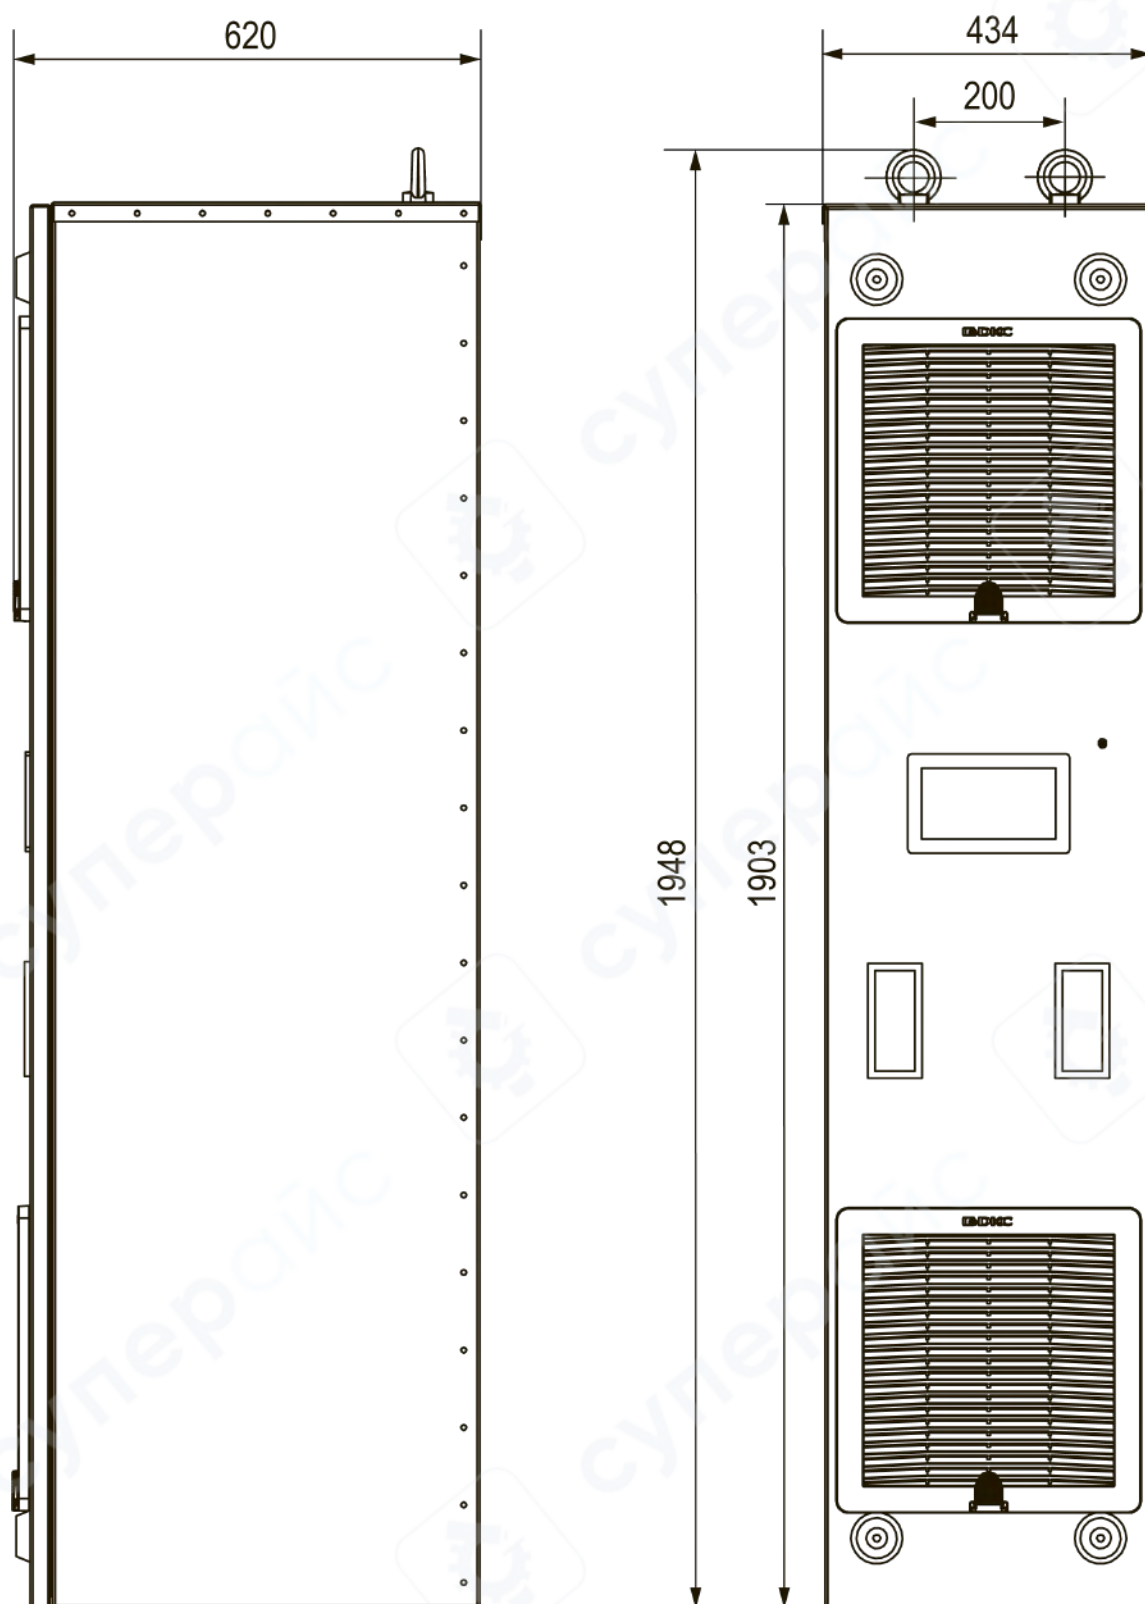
Габаритные размеры прибора в корпусе типоразмера 21
